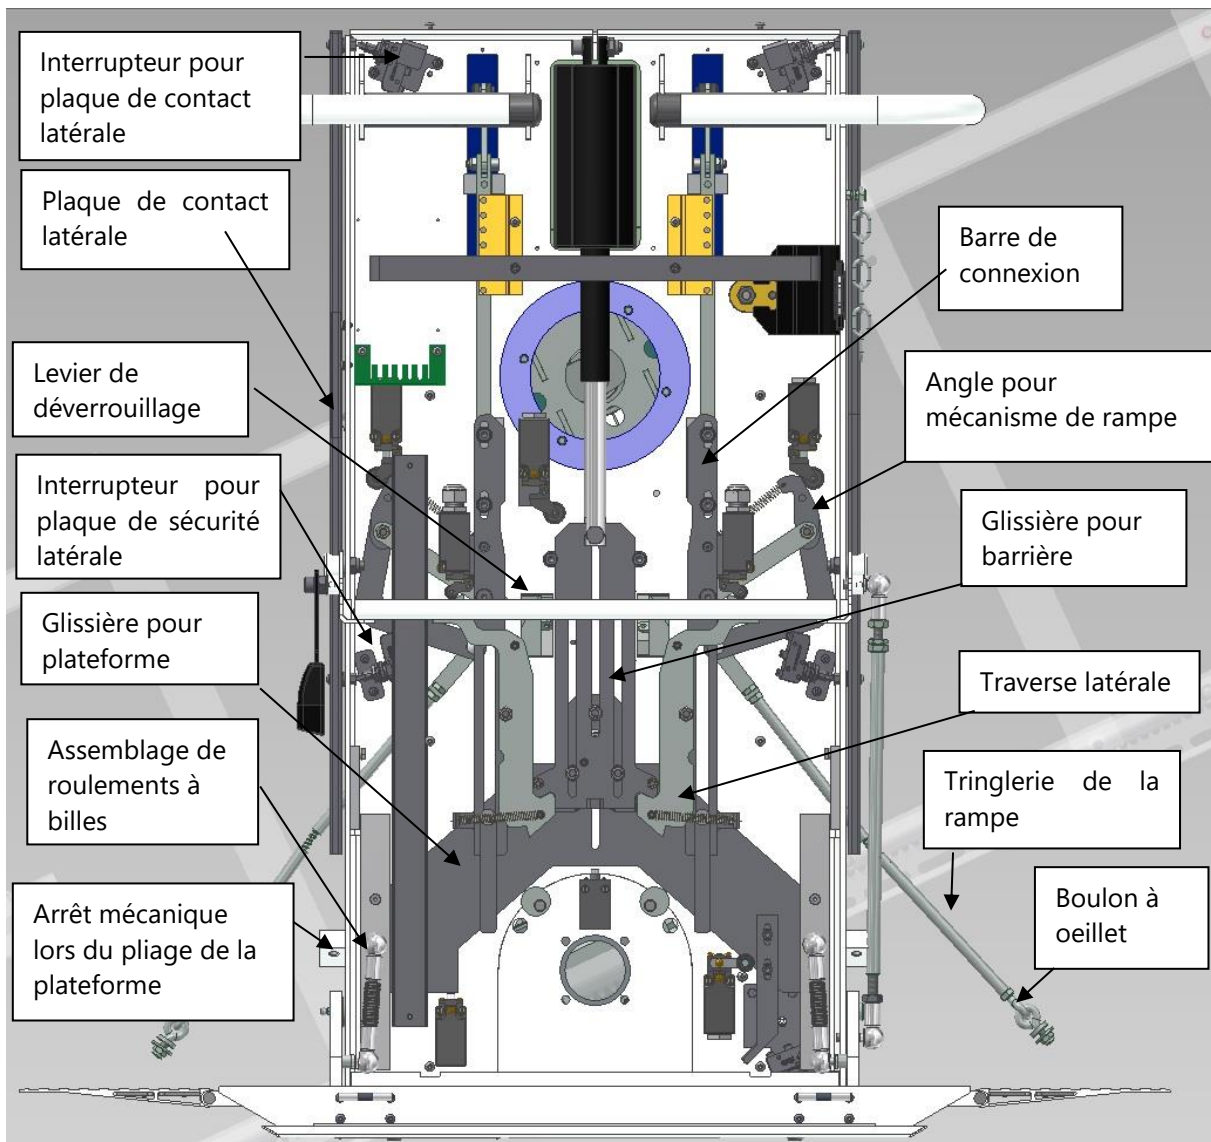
Vue d'ensemble des pièces mécaniques de la plateforme
